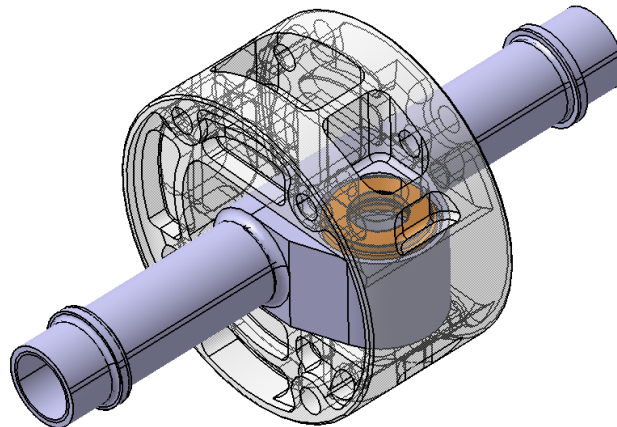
Detalle del apoyo entre buje y eje de dirección.
